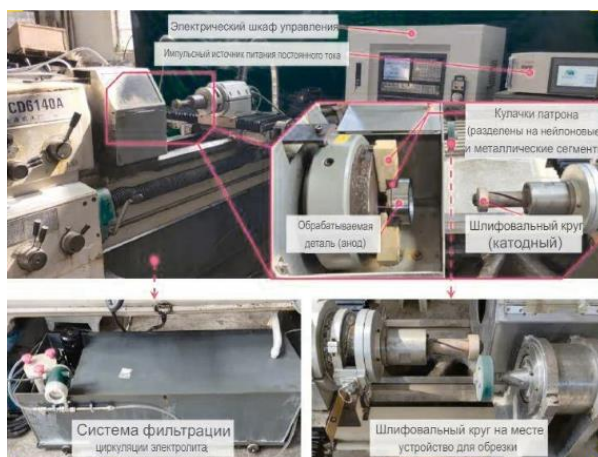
Экспериментальное устройство для электрохимического шлифования внутренней поверхности подшипника
